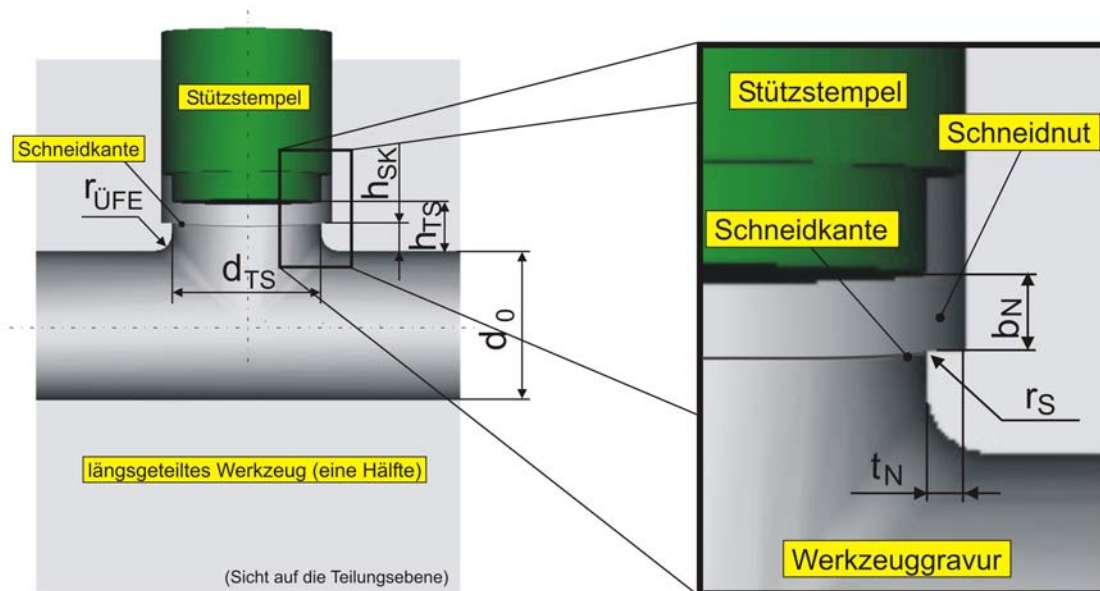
Geometrische Kenngrößen am Werkzeug für das Innenhochdruck-T-Stück-Abschneiden
